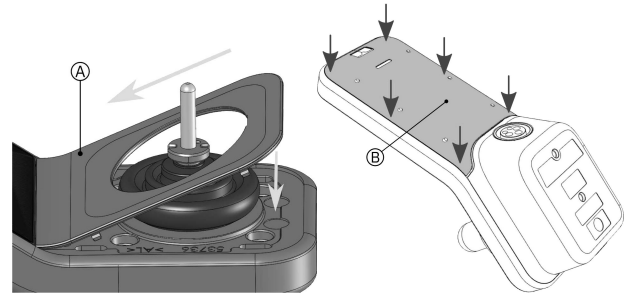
Rimontare il rivestimento decorativo del joystick e la copertura posteriore
